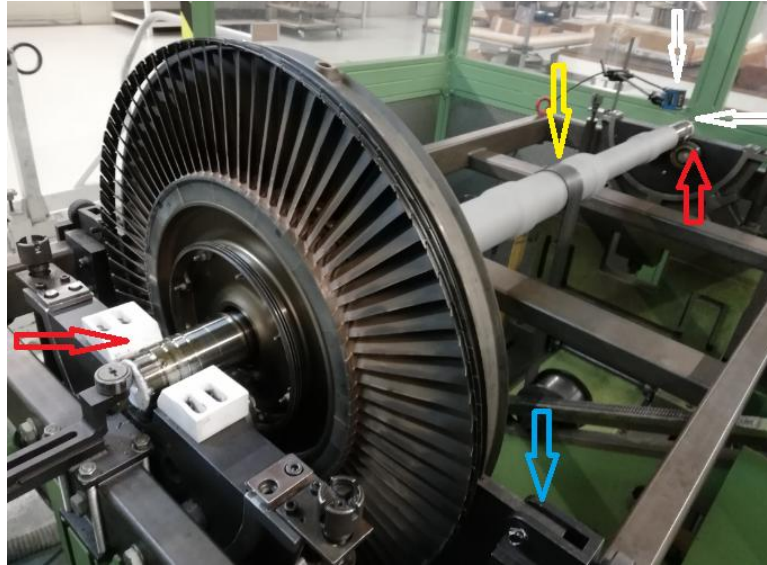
Representa a turbina “LPT” instalada no seu stand de equilibragem.
